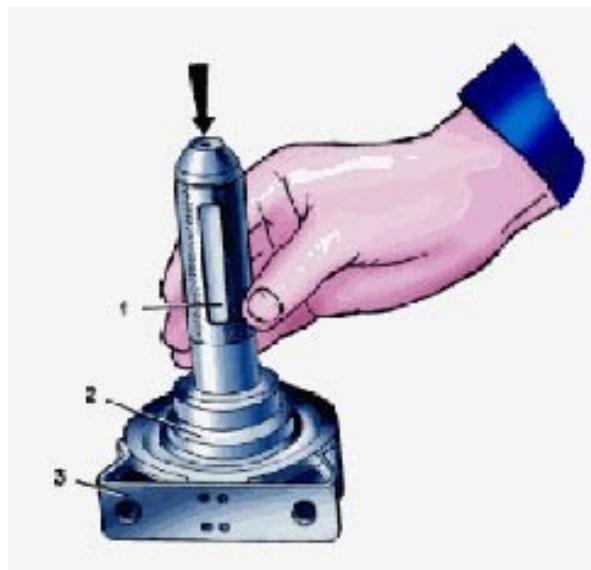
Запресовування підшипника в проміжну опору:
